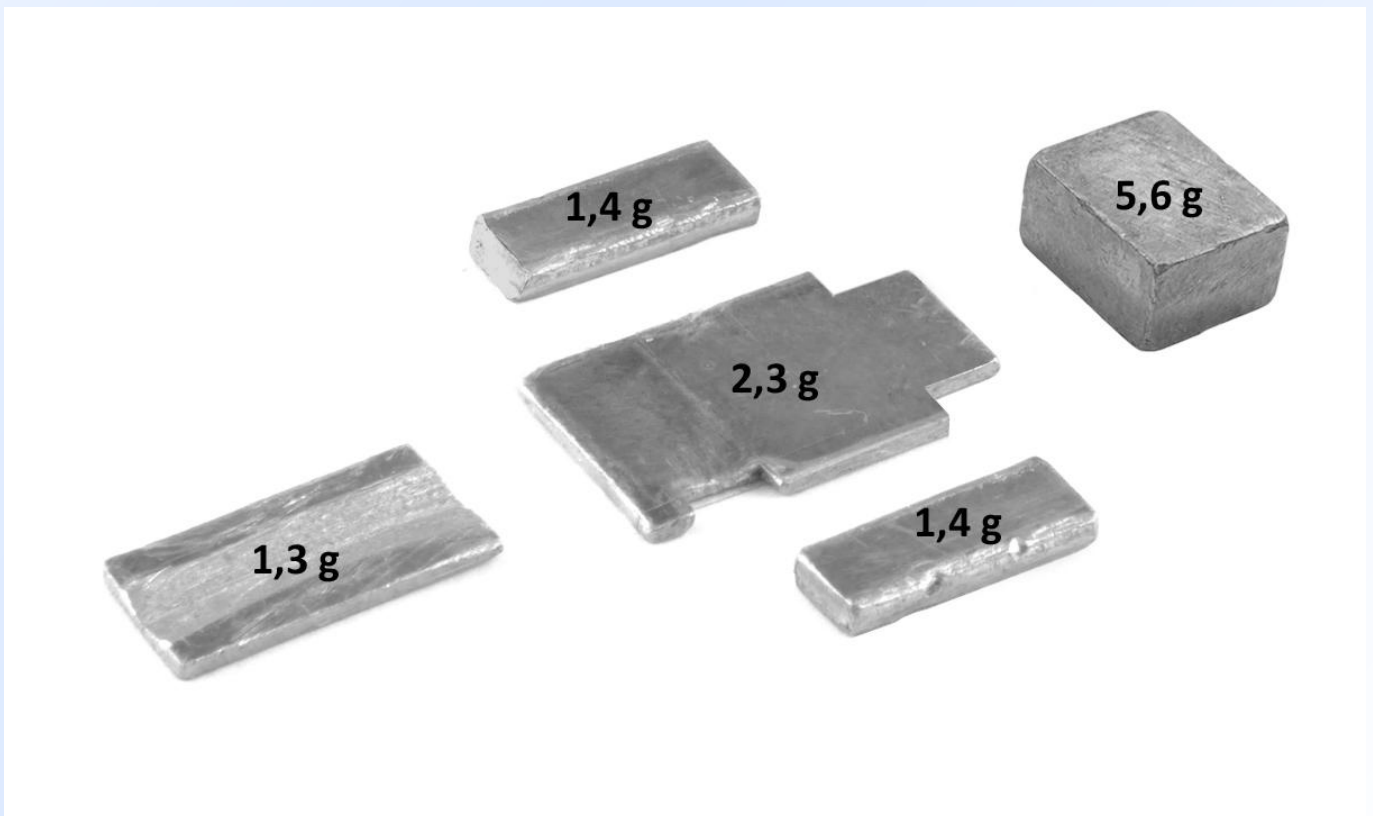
Teile des Zusatzgewichts und ihre Gewichte.
